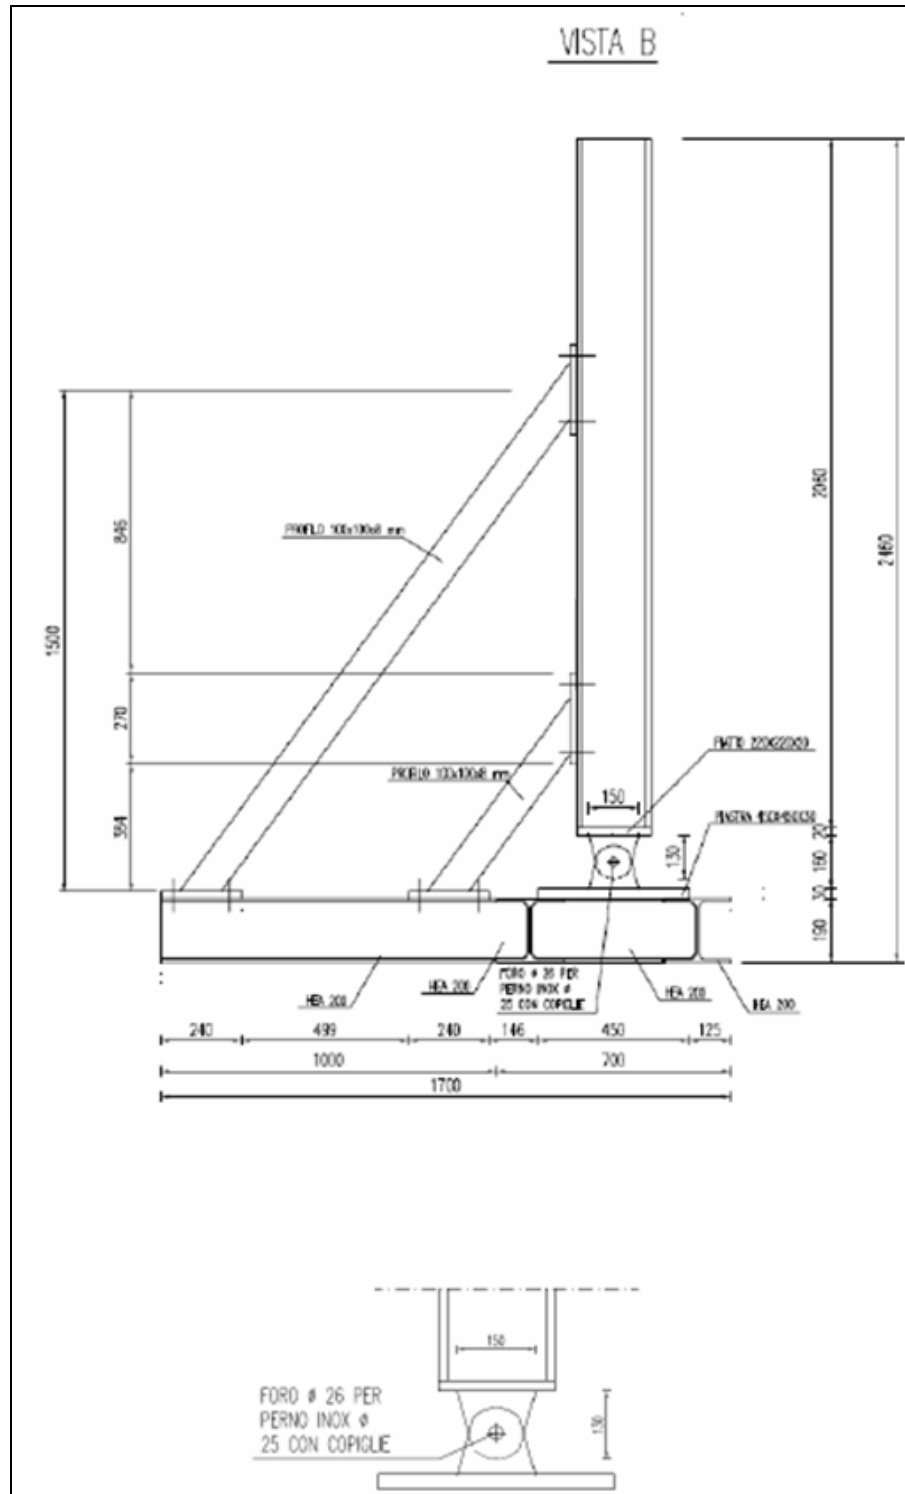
Telaio di supporto campionature per prove a fatica – Vista B
